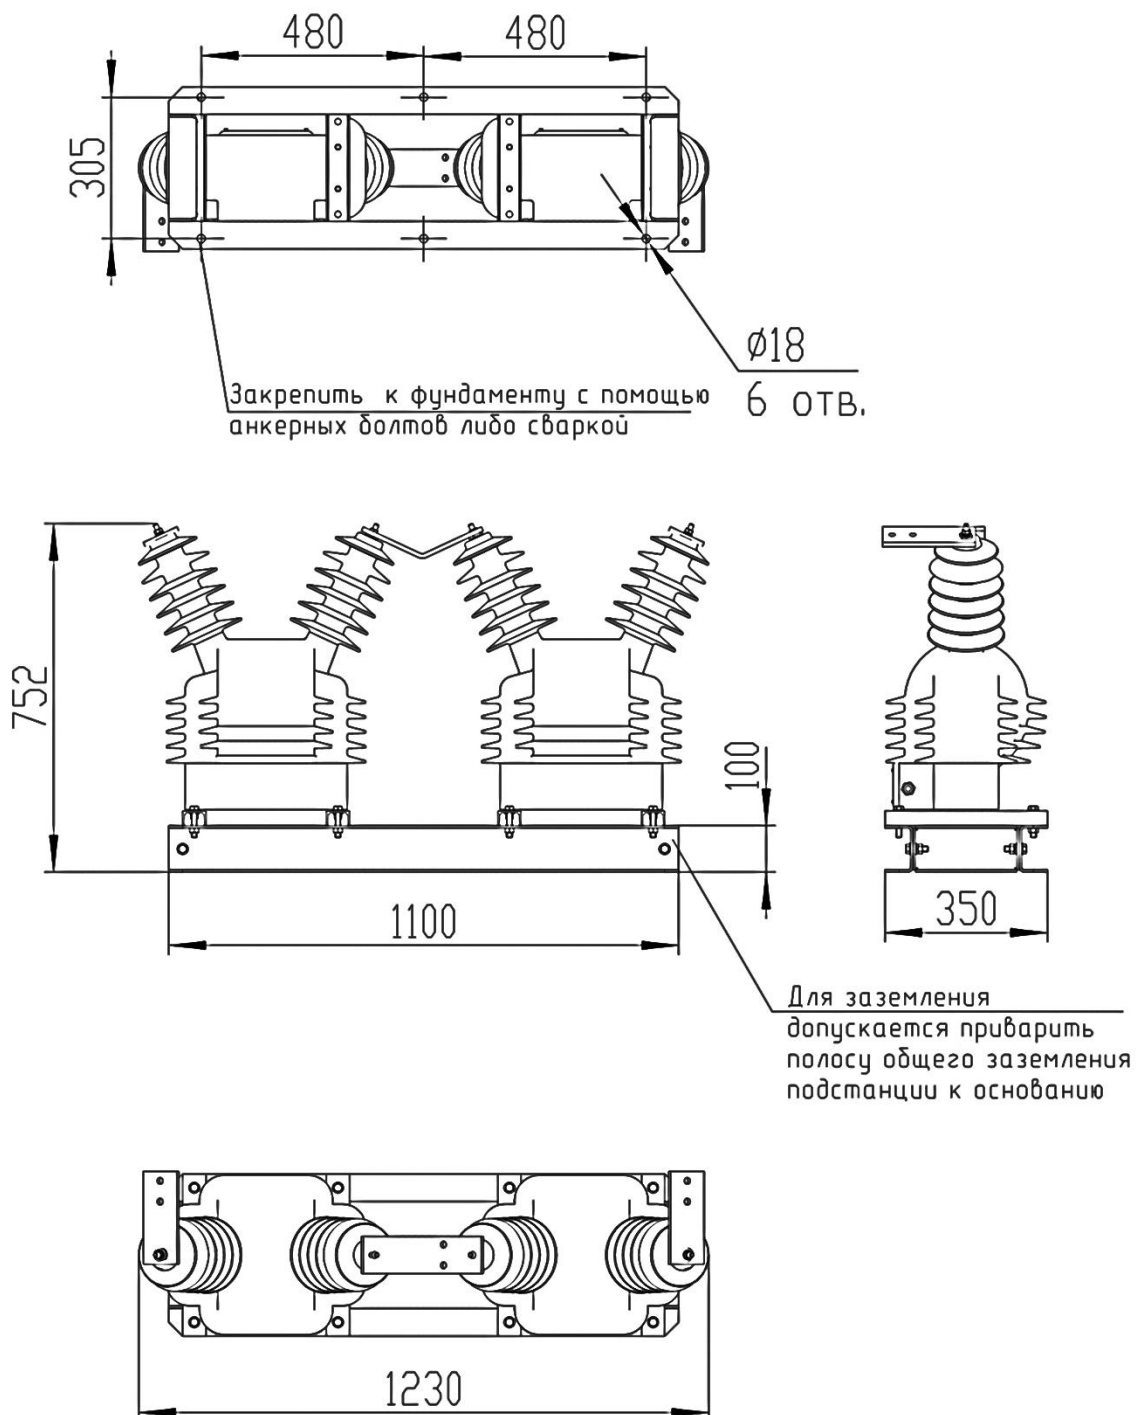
Габаритный чертеж трансформаторов напряжения
